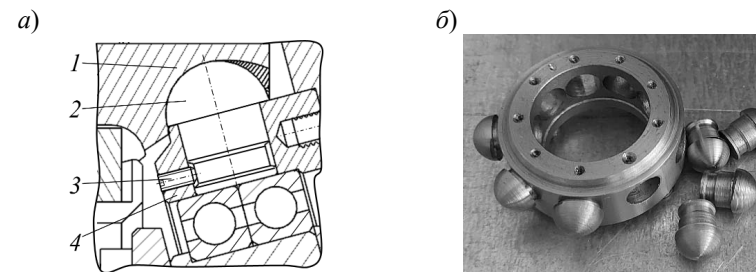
Механизм фиксации ролика: а – схема; б – детали образца
